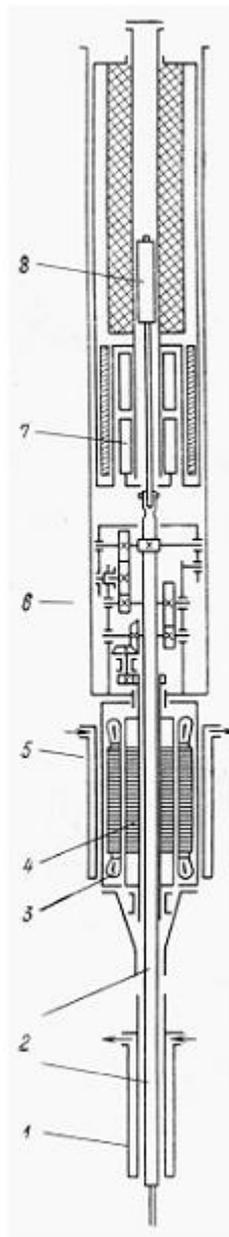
Схема механизма управления ВВЭР-440 (1-я модификация): 1 – охладитель; 2 – рейка; 3 – статор электродвигателя; 4 – ротор электродвигателя; 5 – охладитель; 6 – редуктор; 7 – узел отключателя; 8 – индуктивный датчик положения [1, рис. 3.15]
